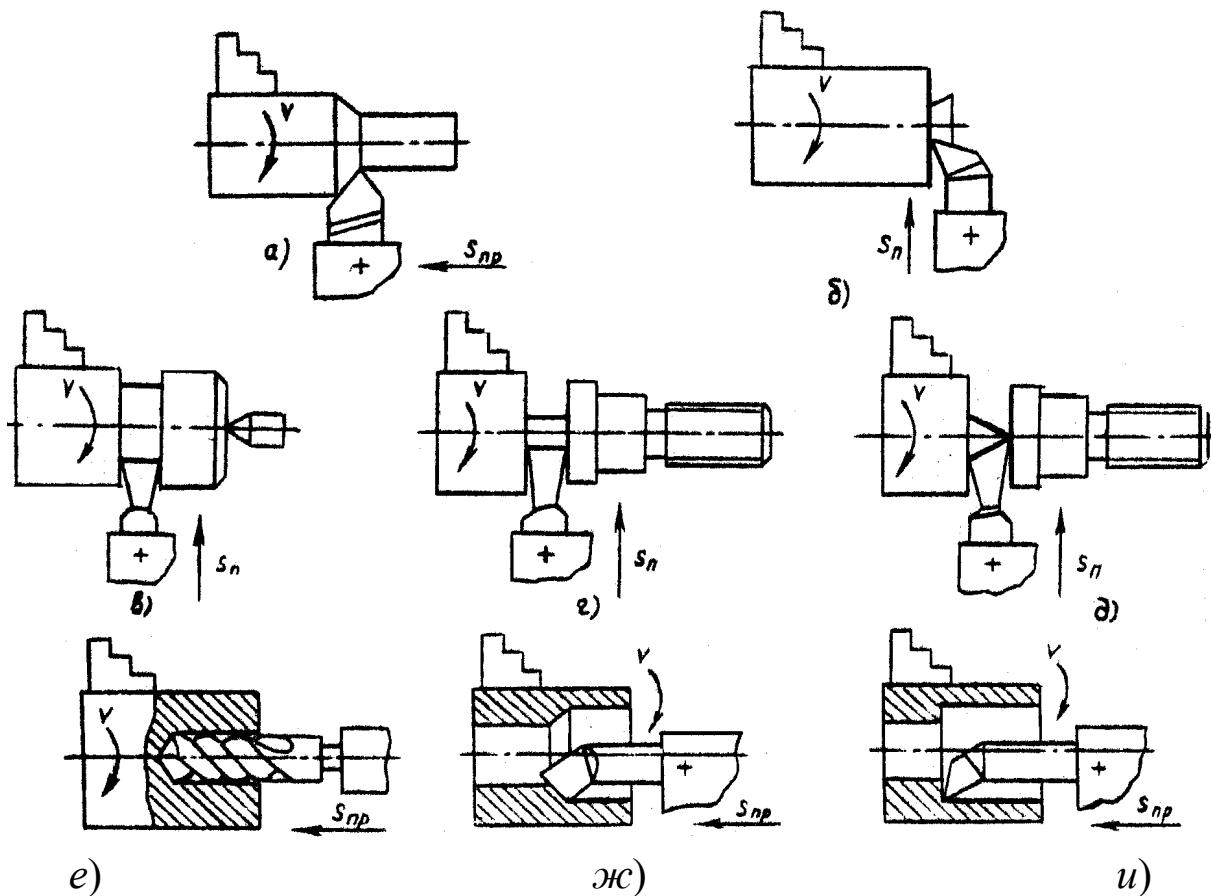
Зображення схем обробки заготовок на токарно-гвинторізних верстатах різцями: прохідний прямий (а); прохідний упорний (б); канавний (в); відрізні (г,д); розточувальний прохідний (ж); розточувальний упорний (и); свердлом (е)
